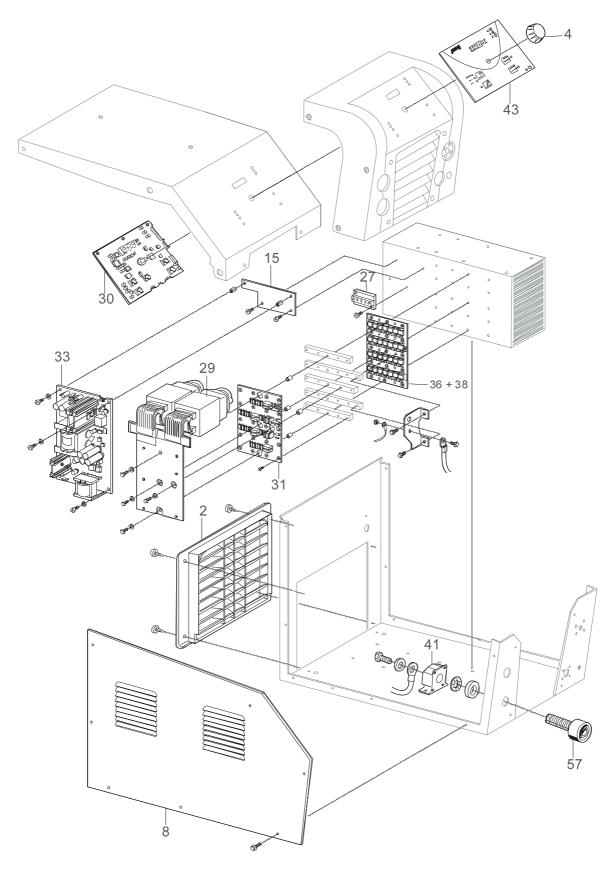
Explosionszeichnung BOOSTER.PRO 250 / 320 (links)
